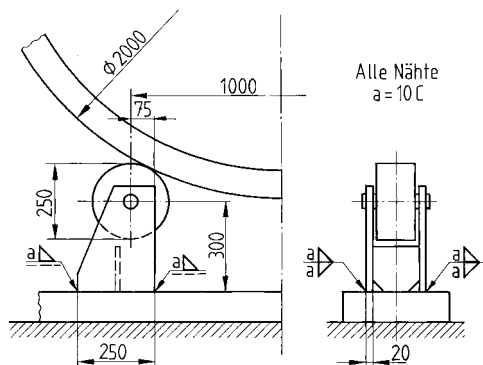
Geschweißter Rollenbock in einer Vorrichtung
